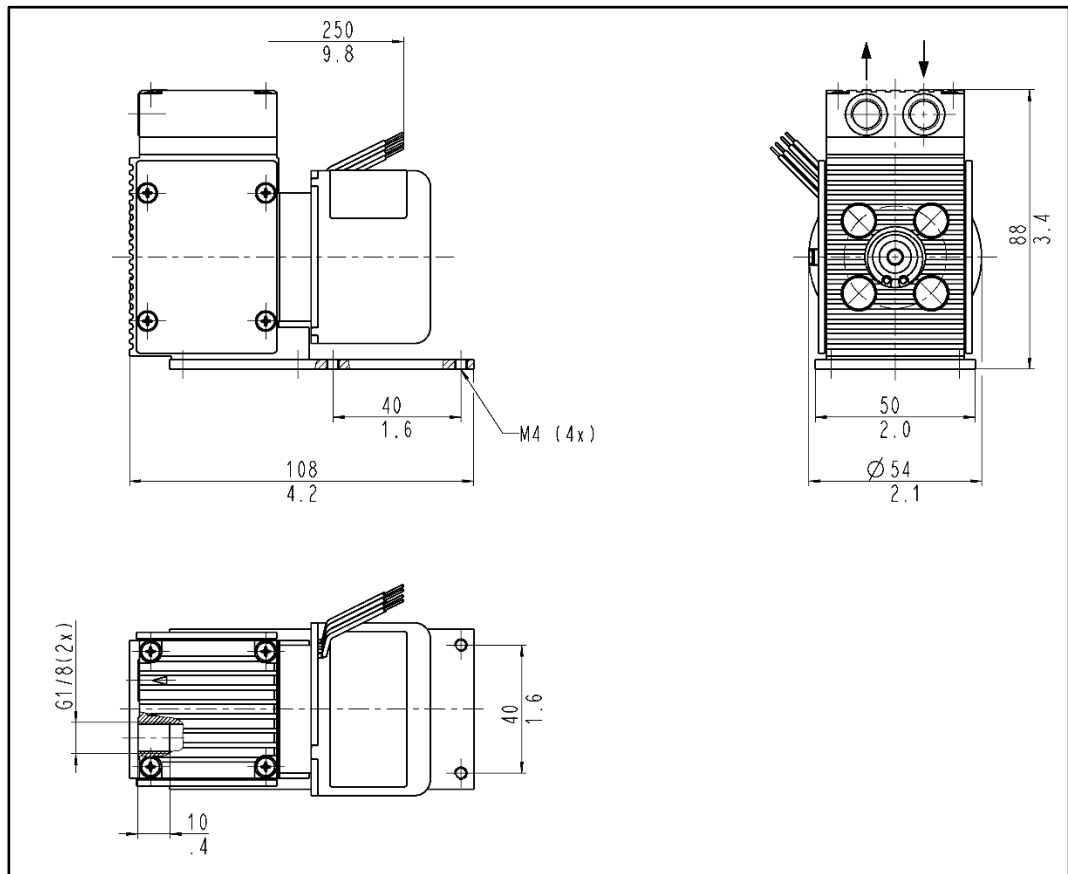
Befestigungsmaße Pumpenreihe N86DC-B
